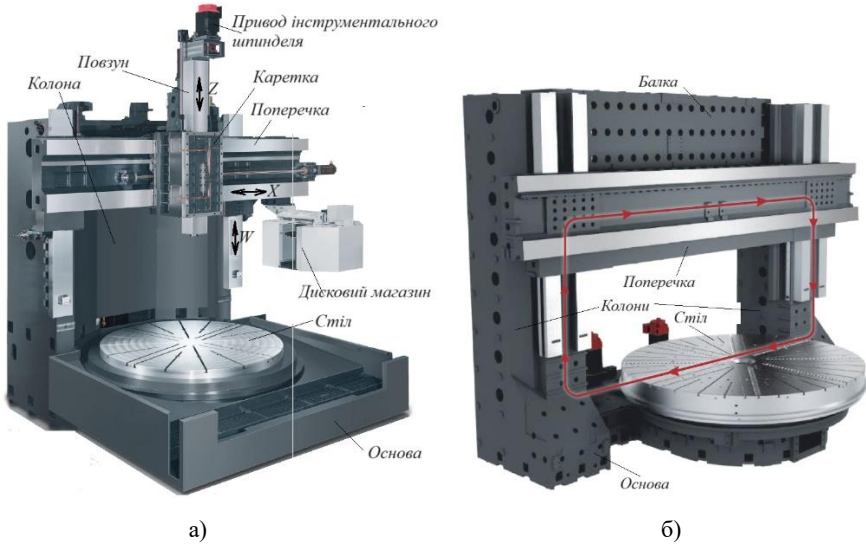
Вертикальний токарний верстат з ЧПК
